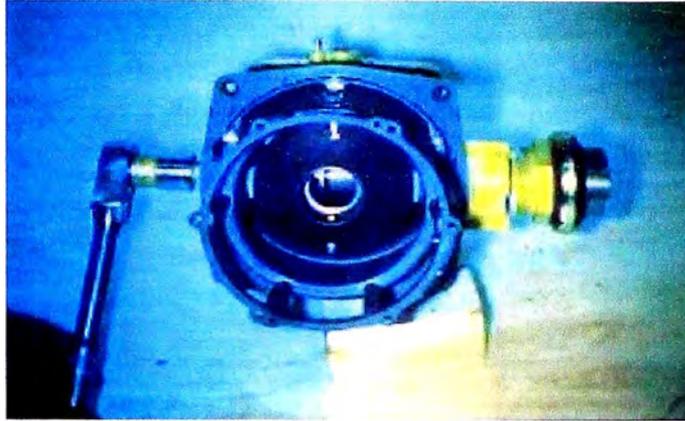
Ajuste del tornillo de mezcla del carburador.
